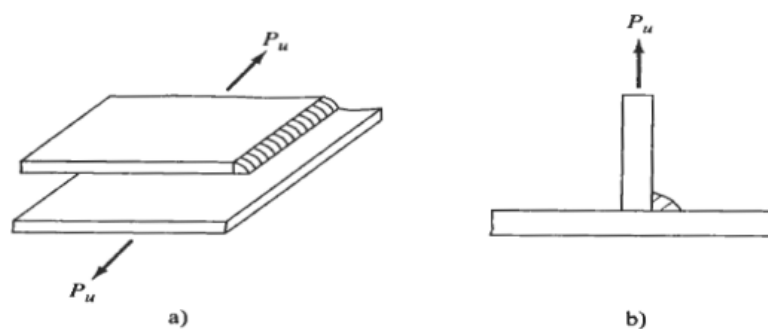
a) soldadura de filete longitudinal b) soldadura de filete transversal
